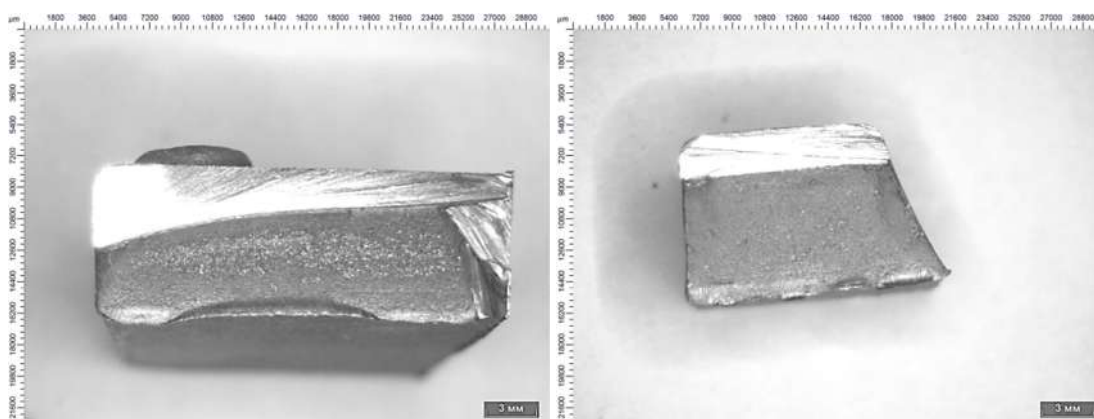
Излом плавки № 27 (а) и № 33 (б) из стали 35ХГСЛ (раскислитель СК30)
